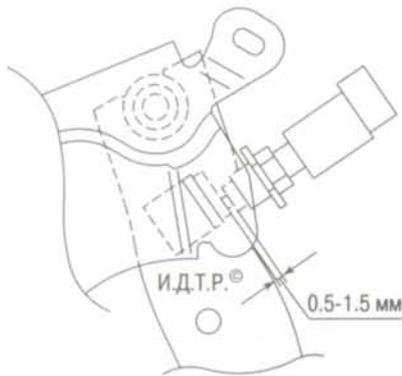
Регулировка зазора датчика выключения сцепления
